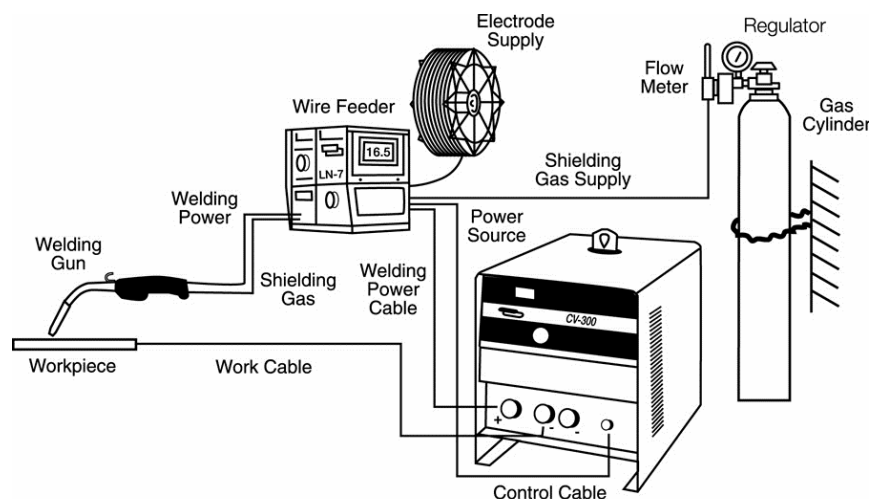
Equipos para soldadura MIG-MAG [15].
